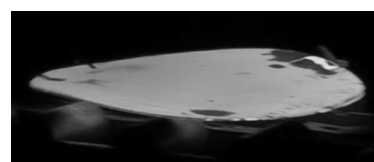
Заготовки после нагрева в газовой печи до 1100 °C.
